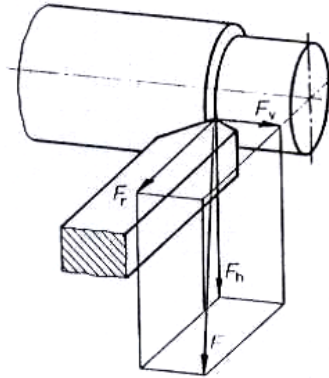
Fuerzas que ejerce la pieza sobre la herramienta.
